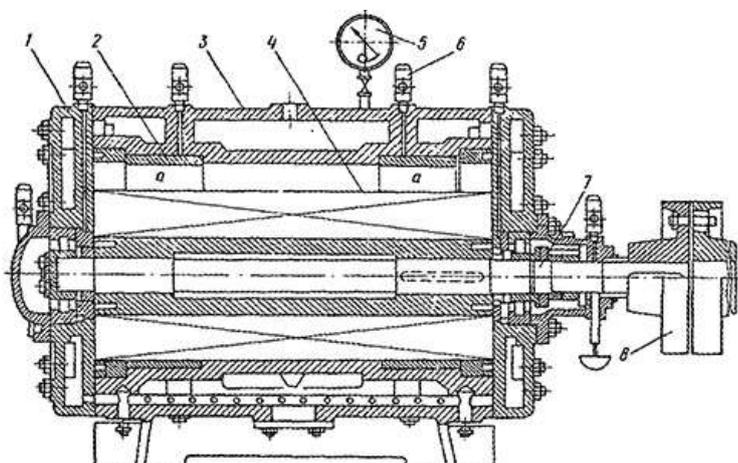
Вид пластинчатого компрессора
